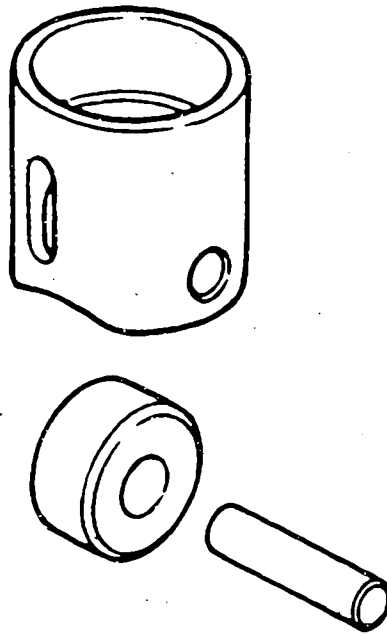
Rollenstößel, Rolle und Lagerbolzen
